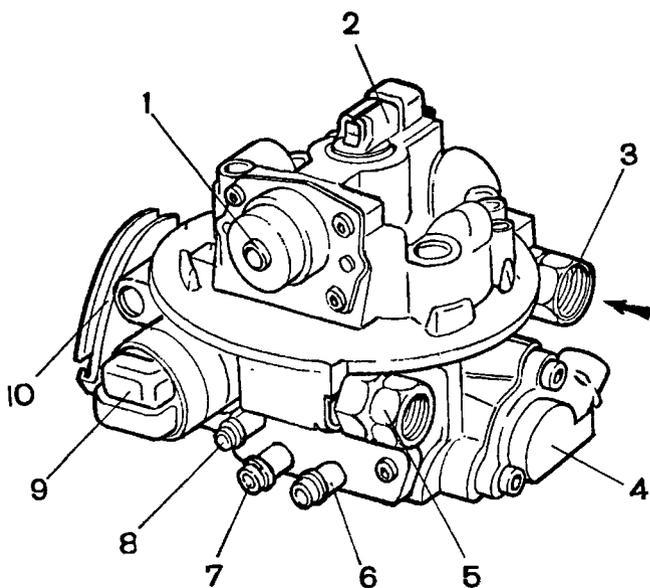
Агрегат центрального впрыска: 1 - регулятор давления топлива; 2 - форсунка; 3 - штуцер подвода топлива; 4 - датчик положения дроссельной заслонки; 5 - штуцер отвода топлива в бак; 6 - патрубок продувки адсорбера; 7 - патрубок вентиляции картера двигателя; 8 - патрубок подсоединения датчика абсолютного давления; 9 - регулятор холостого хода; 10 - сектор привода дроссельной заслонки от педали в салоне автомобиля
